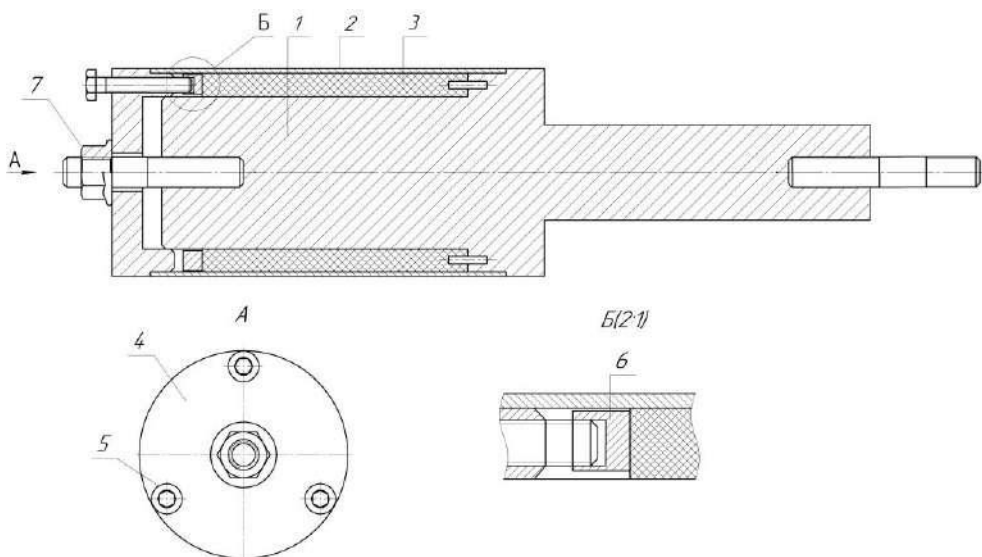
Схема крепления оправки к делительной головке станка
